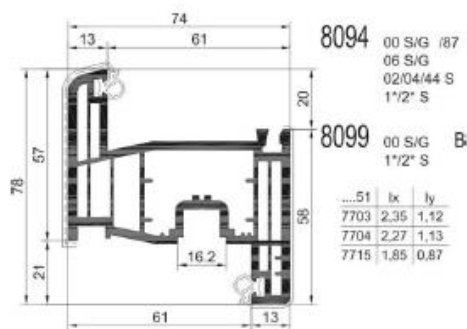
Planșa în secțiune transversală a cercevei (Cat. No. 8094.00) profile PVC.
